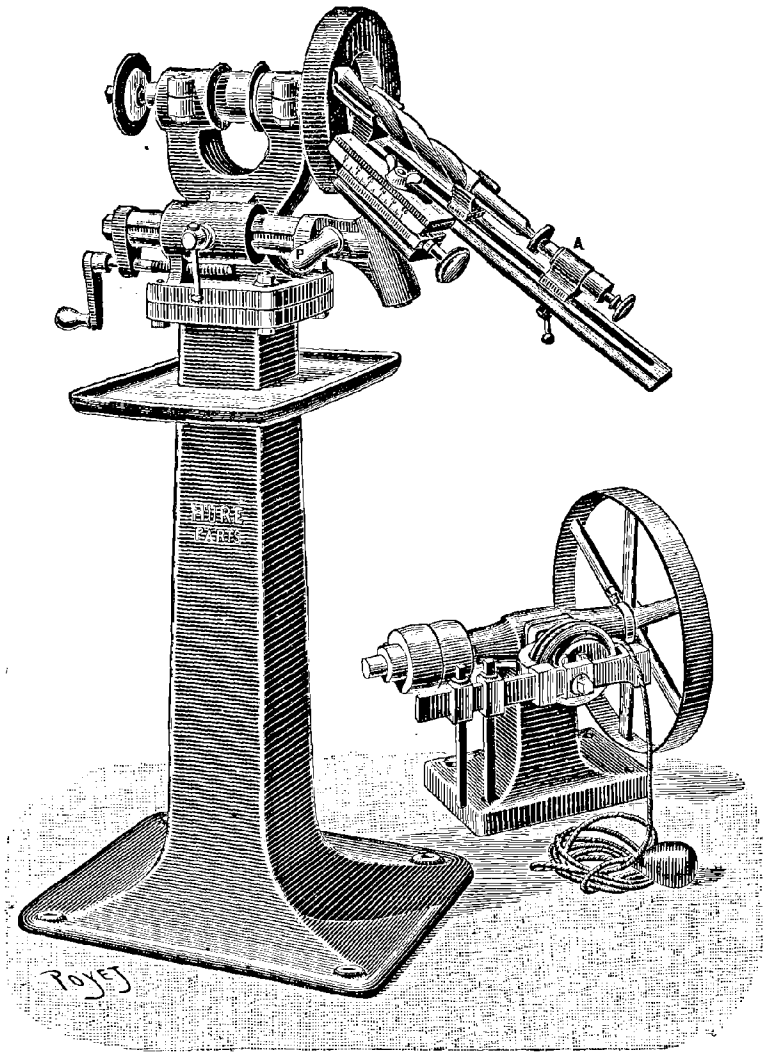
Machine à affûter les forets hélicoïdaux de M. Huré.
